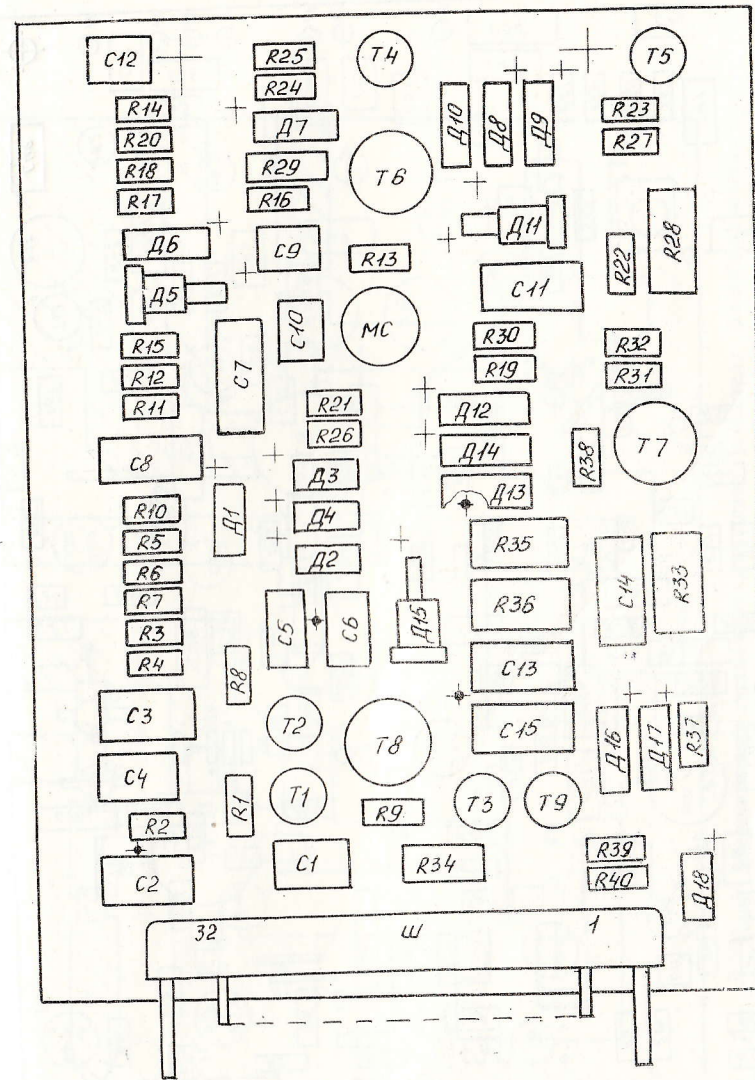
План расположения элементов на плате усилителя системы АРМ
